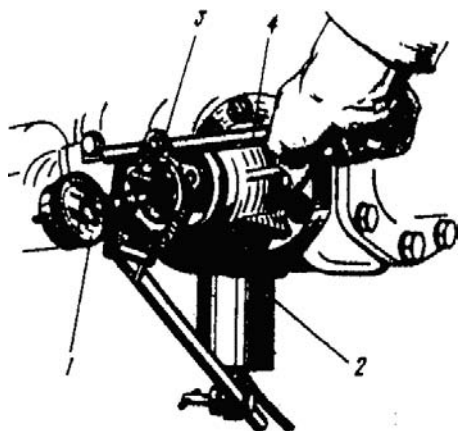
Проверка осевого зазора в подшипниках ведущей шестерни главной передачи переднего ведущего моста.
